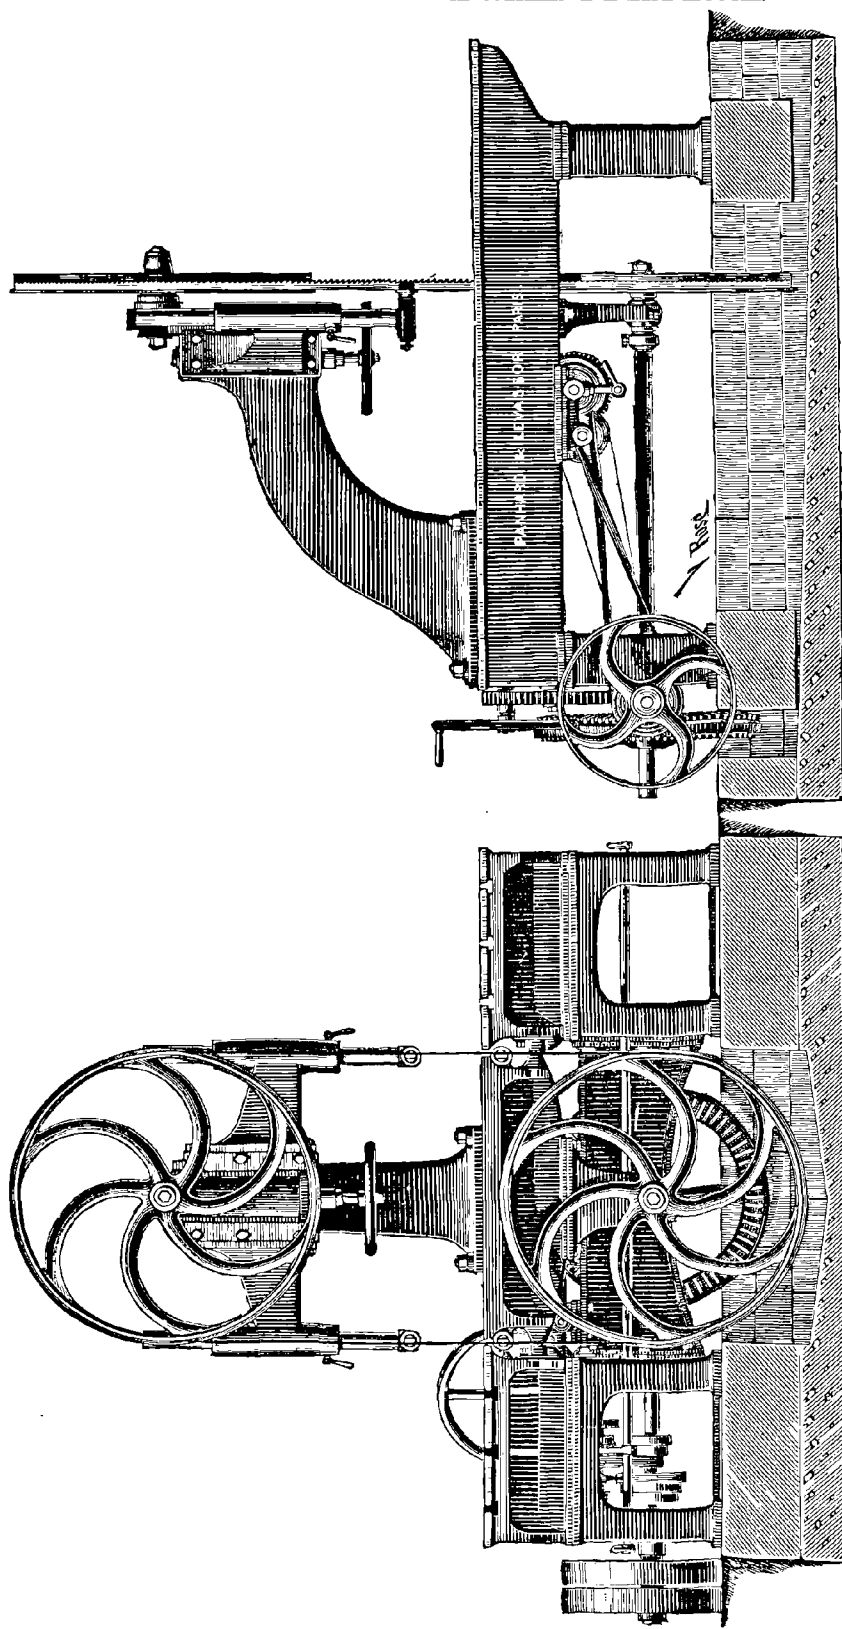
Scie à ruban à double table de Panhard et Levassor. — Vue de côté.
